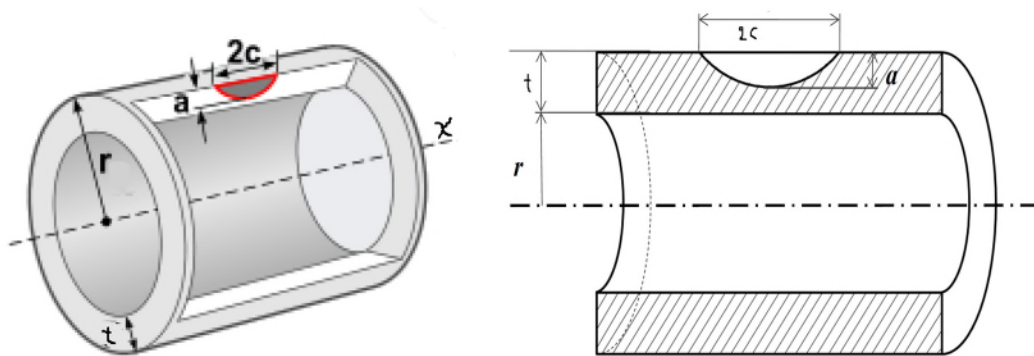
fissure longitudinale à l'extérieur de la conduite
